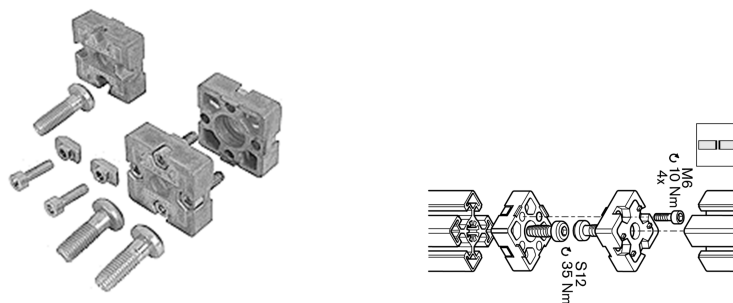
Acessório End Connector [imagem adaptada de [12]]
